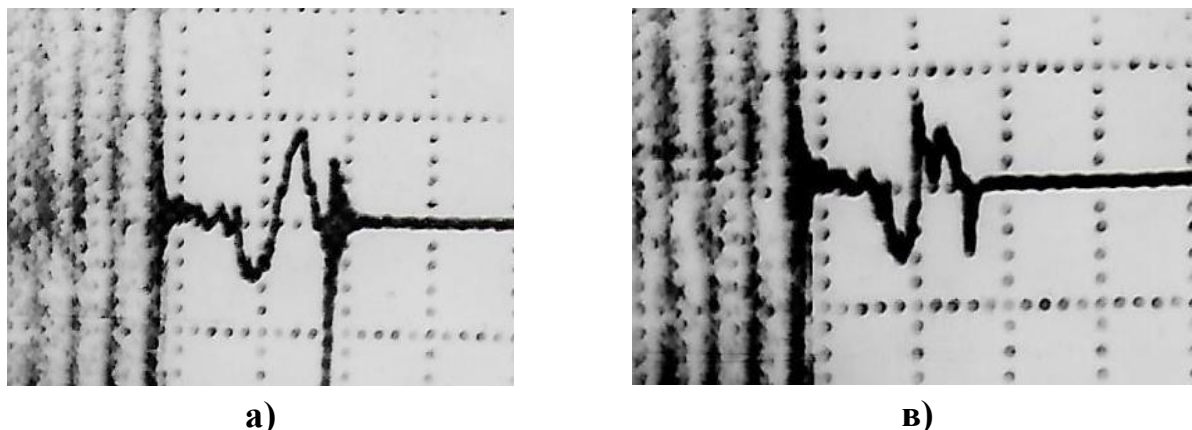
Акустический сигнал с пьезодатчика в момент отрыва инструмента при формировании а) качественного сварного соединения, в) отсутствие качественной микросварки
